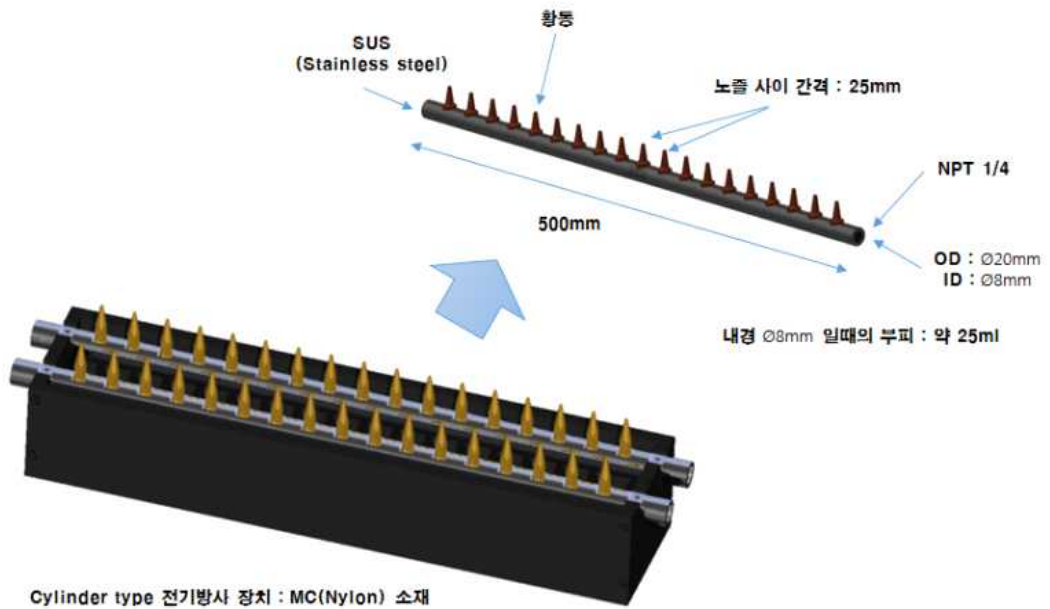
3D Tool을 이용한 Multi-nozzle 조립성 검토 및 가공성 확인 완료
